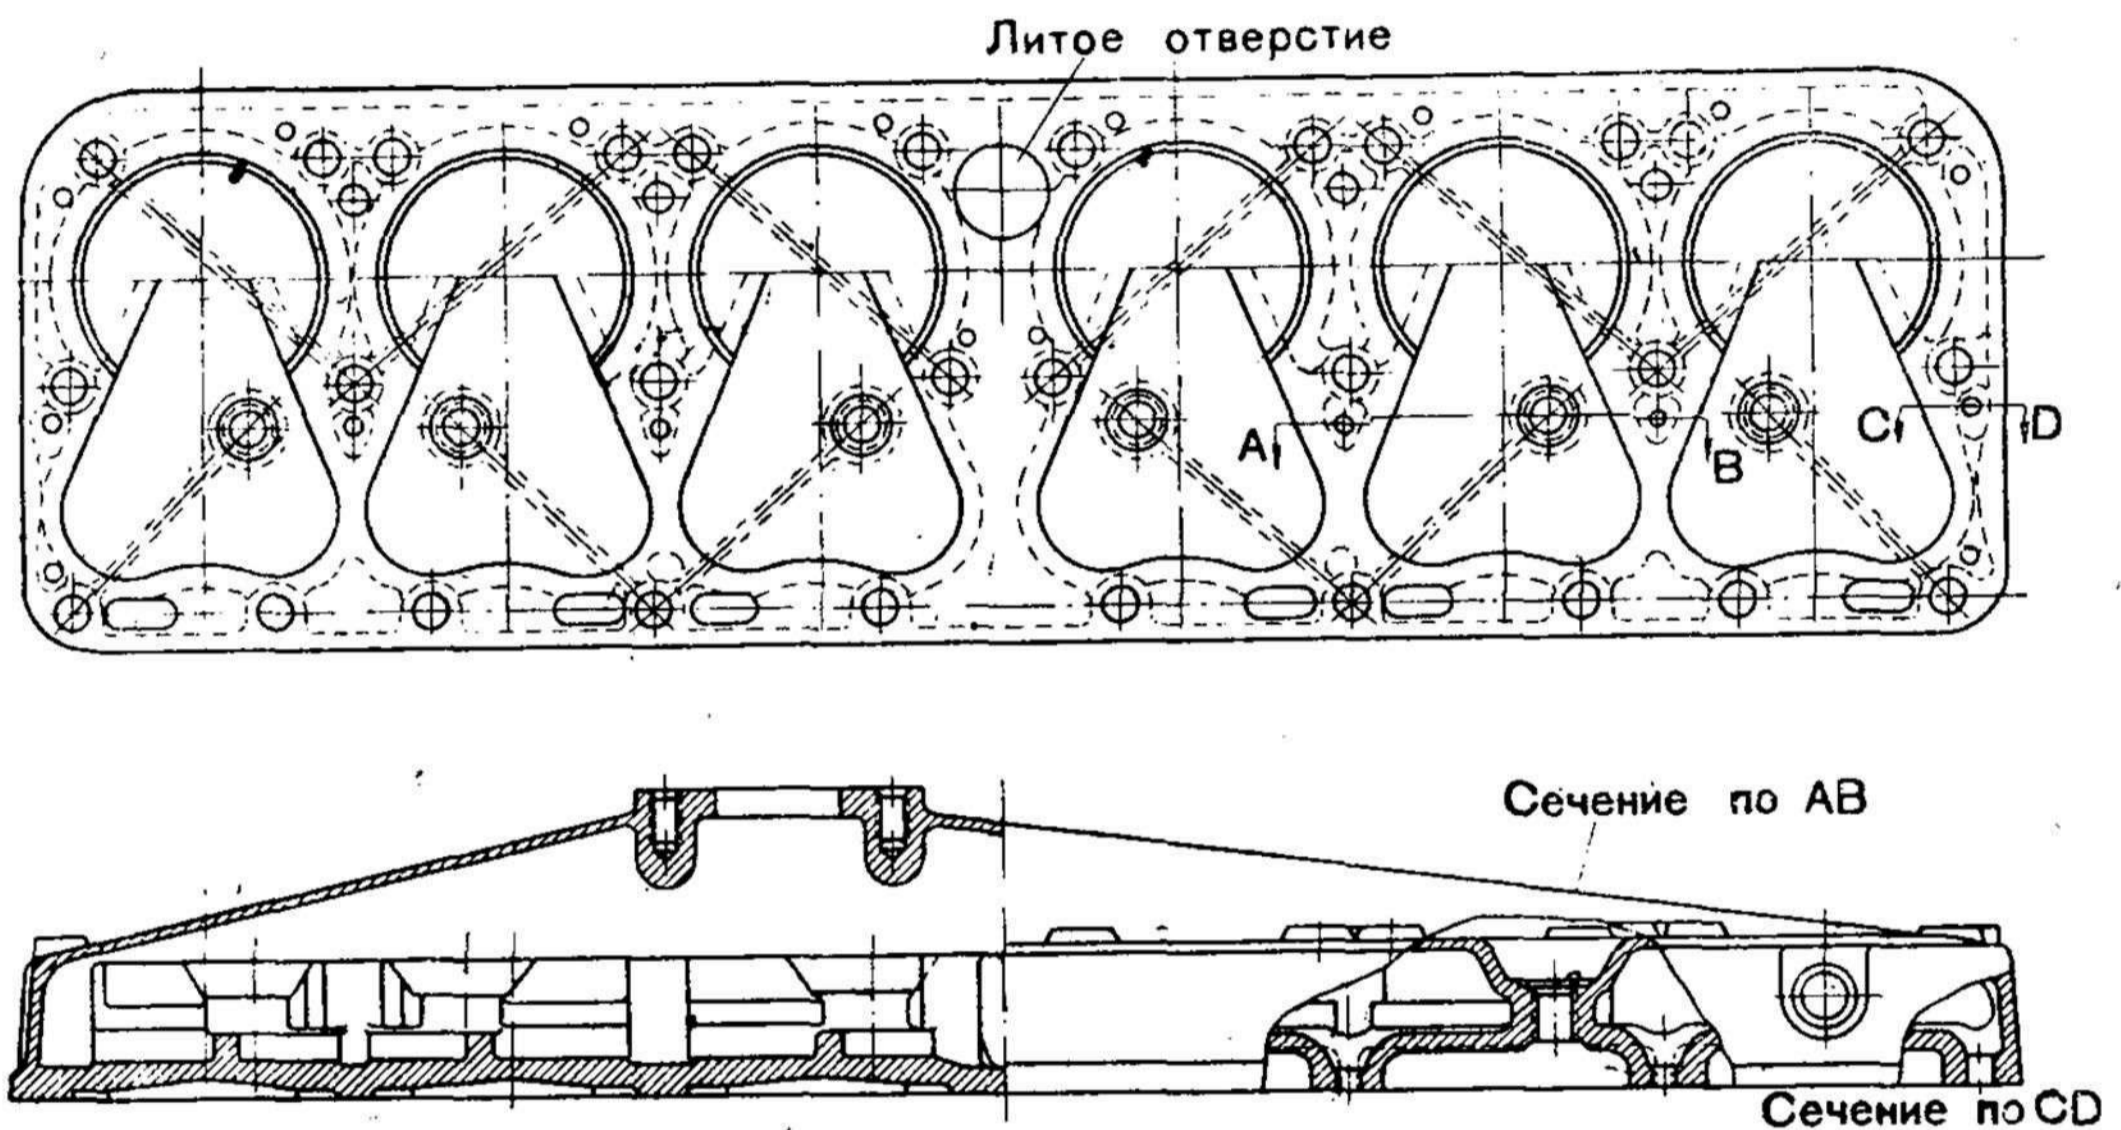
Головка блока цилиндров двигателя ЗИС-13.
